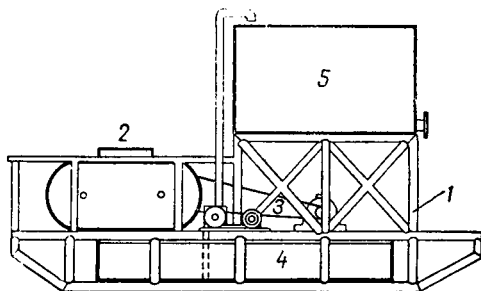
Передвижная установка для приготовления щелочных реагентов.
